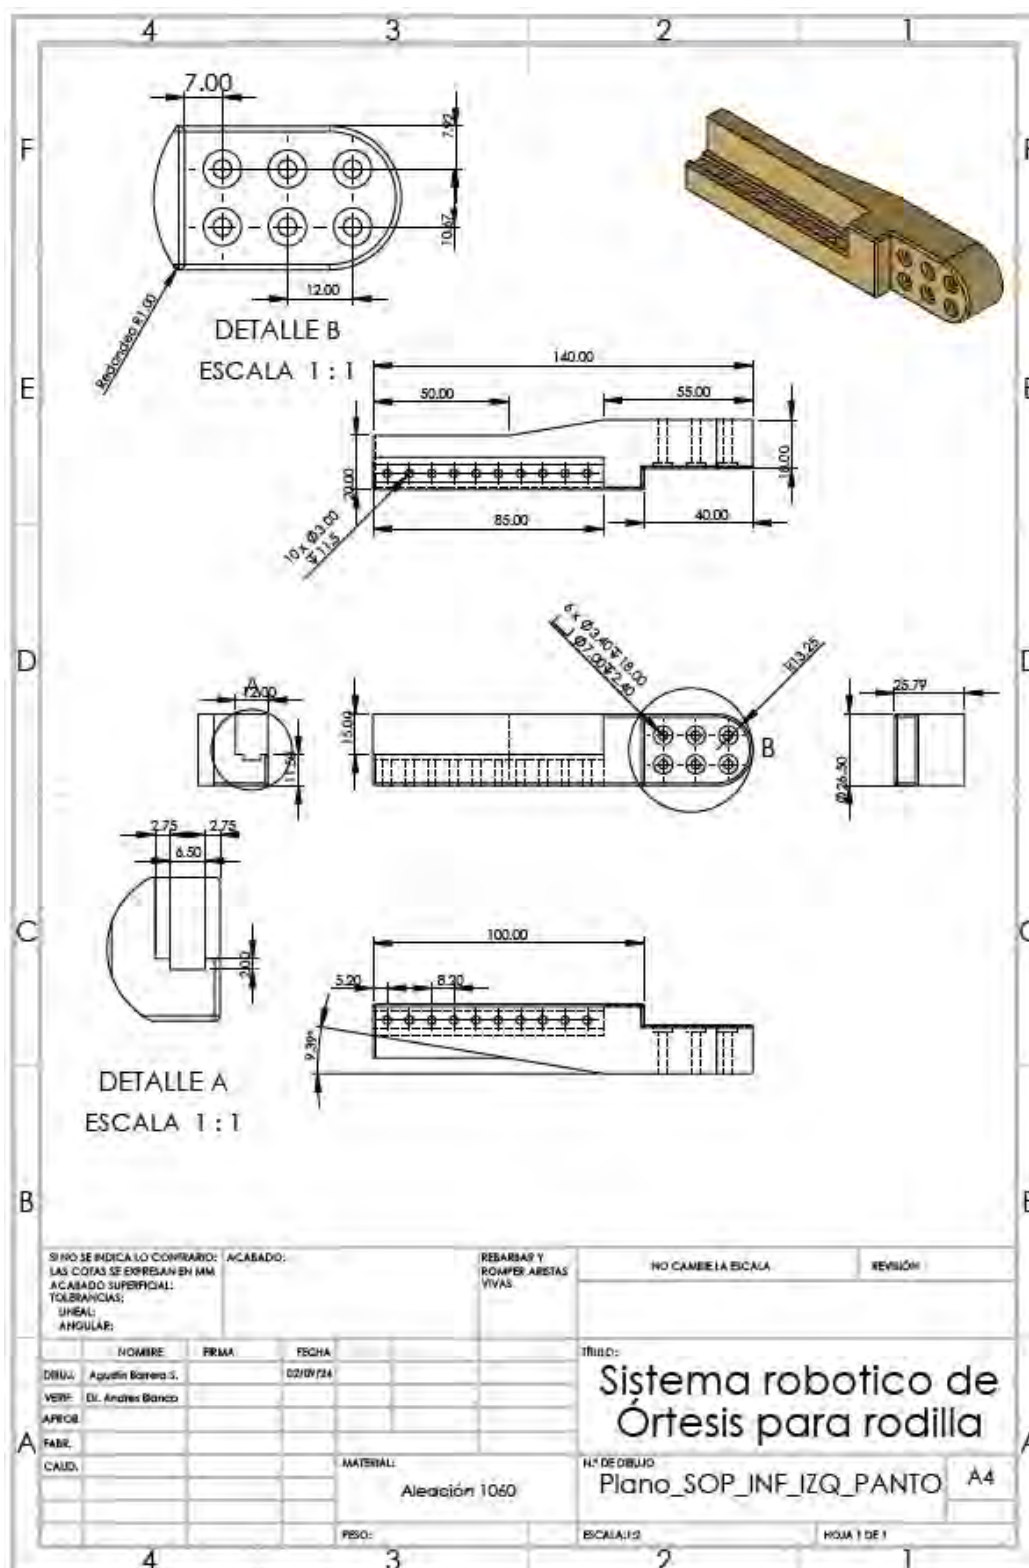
Dibujo de detalle: Estructura ajustable pantorrilla inferior-lado exterior.
